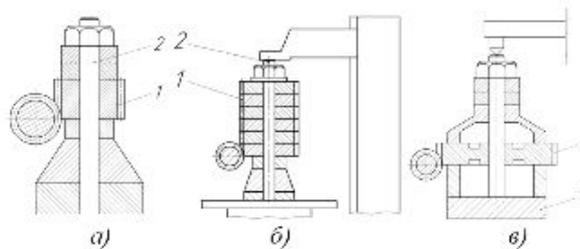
Типовые способы крепления заготовок на зуборезных станках:
